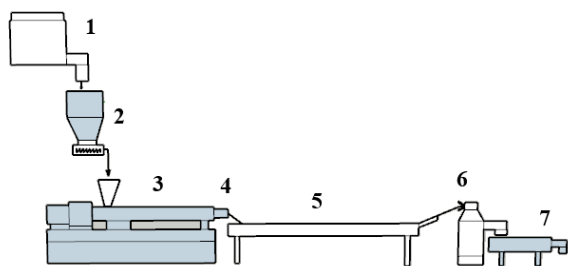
Схема приготовления концентрата дисульфида молибдена (КДМ): 1 — смеситель; 2 — дозатор; 3 — двухшнековый экструдер; 4 — гранулирующая головка; 5 — ванна охлаждения; 6 — режущее устройство; 7 — классификатор
